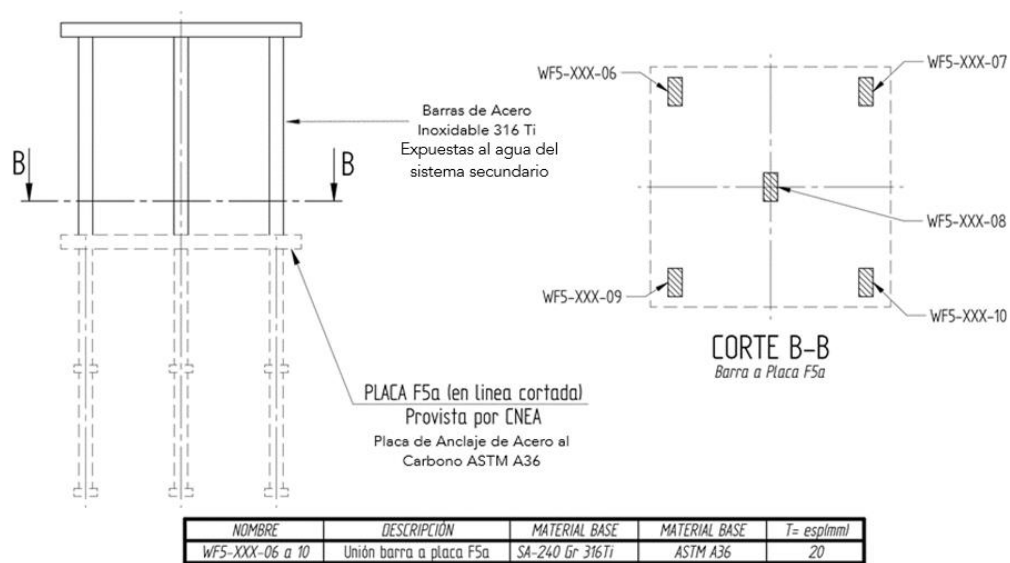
Se detallan las soldaduras entre las barras de unión de Acero Inoxidable AISI 316Ti y la placa de anclaje de Acero al Carbono ASTM A36.
